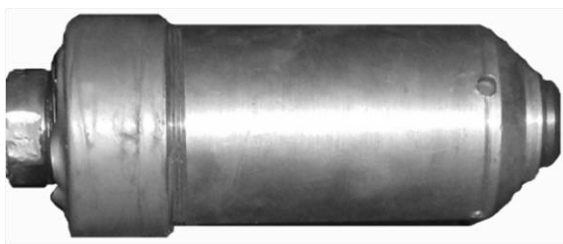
Дуговой плазмотрон ПМВР-2М для резки металлов под сварку
